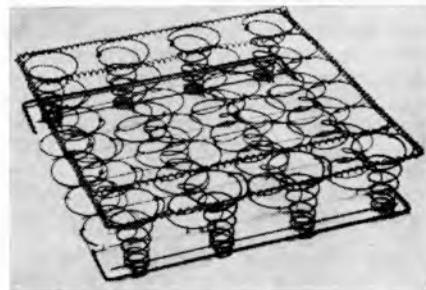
Пружинный блок фирмы «Webster Spring Co»
